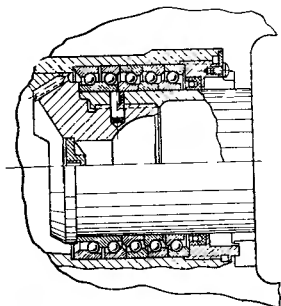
Схема крепления лопасти во втулке на одном шариковом (роликовом) подшипнике.
